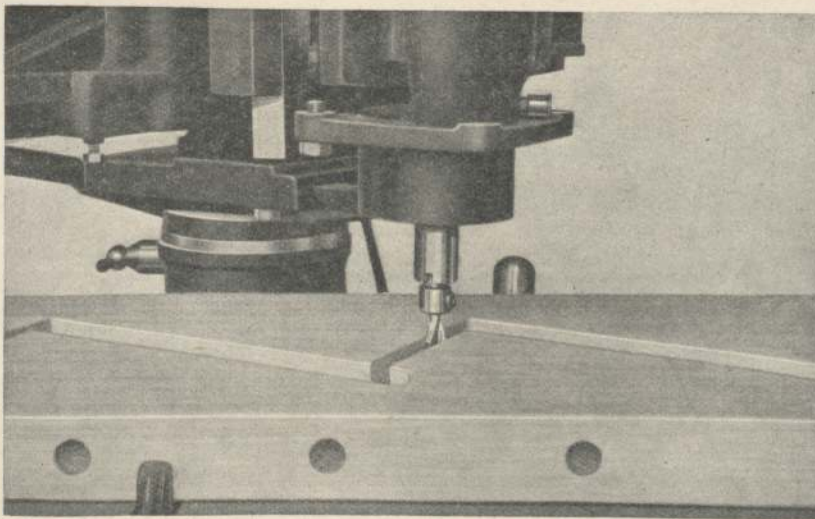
Unterer Motor und Frästeil der „Ruga“-Maschine, eingestellt zum Fräsen der Futterbrettlöcher.
